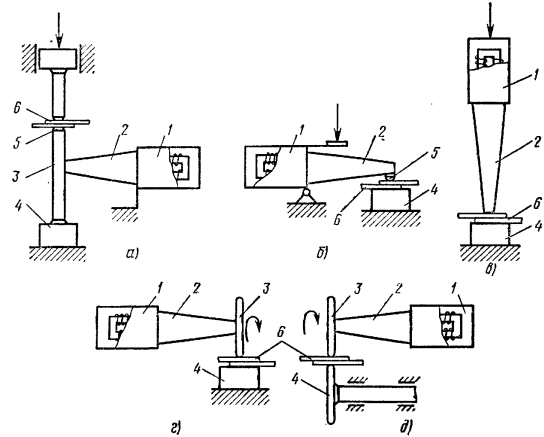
Механические колебательные системы для точечной (а, б) и шовной (в, д) сварки, а также сварки пластмасс (е):
